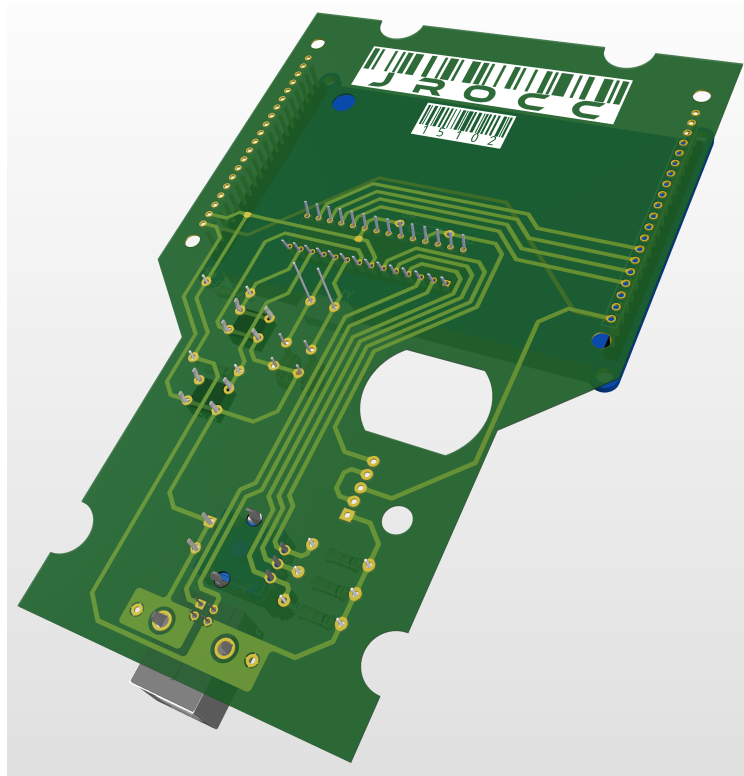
Vista isométrica trasera 3D del prototipo 1 de la PCB
